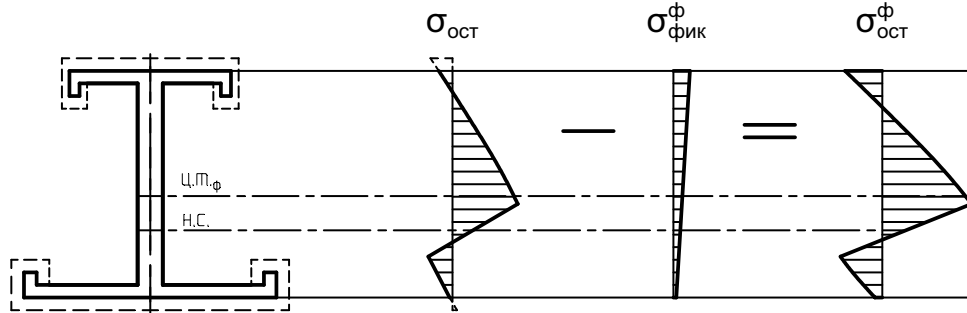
Эпюры напряжений в поперечном сечении заготовки до и после фрезерования
